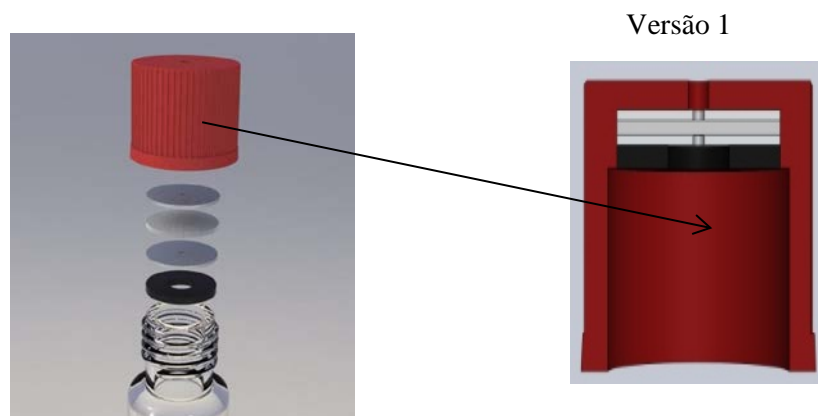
Esquema de vedação das fugas de R134a. Junto ao gargalo uma anilha de neopreno, a membrana de MVQ entre anilhas metálicas perfuradas. A imagem da esquerda ilustra uma ampliação e uma vista do interior da tampa. São visíveis duas anilhas metálicas furadas ao centro, a membrana de permeação e o vedante (anilha de neopreno).
